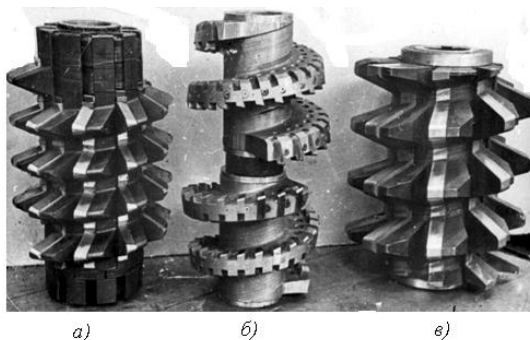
Крупномодульные стандартные быстрорежущие червячные фрезы
